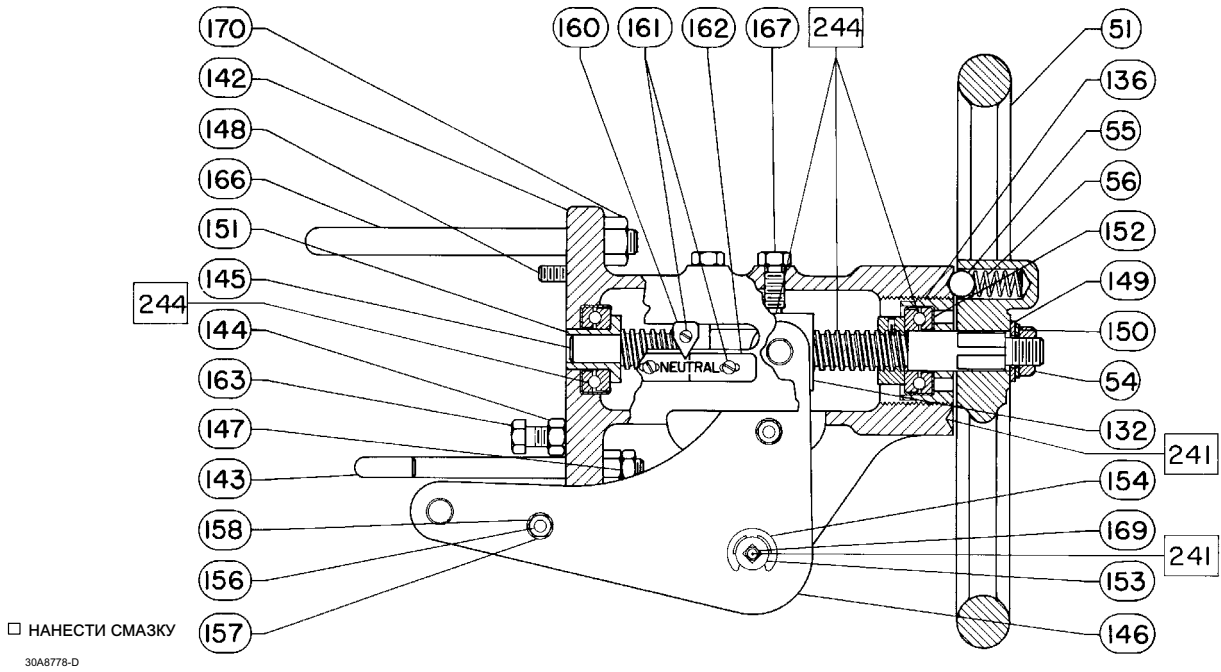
Узел маховика с боковой установкой для приводов размером 34i и 40i
